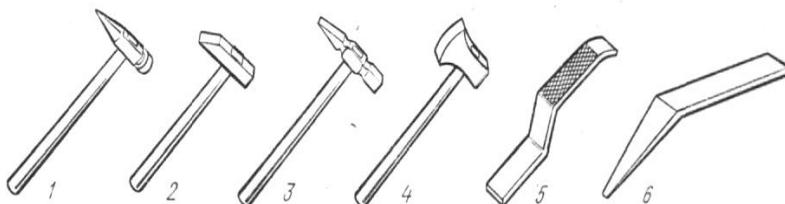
Молотки: 1-рихтовочный; 2-облегчённого типа; 3- для загибки фланцев; 4-с выпуклой ударной частью; 5-специальный с насечкой рабочей части; 6-молоток-гладилка
